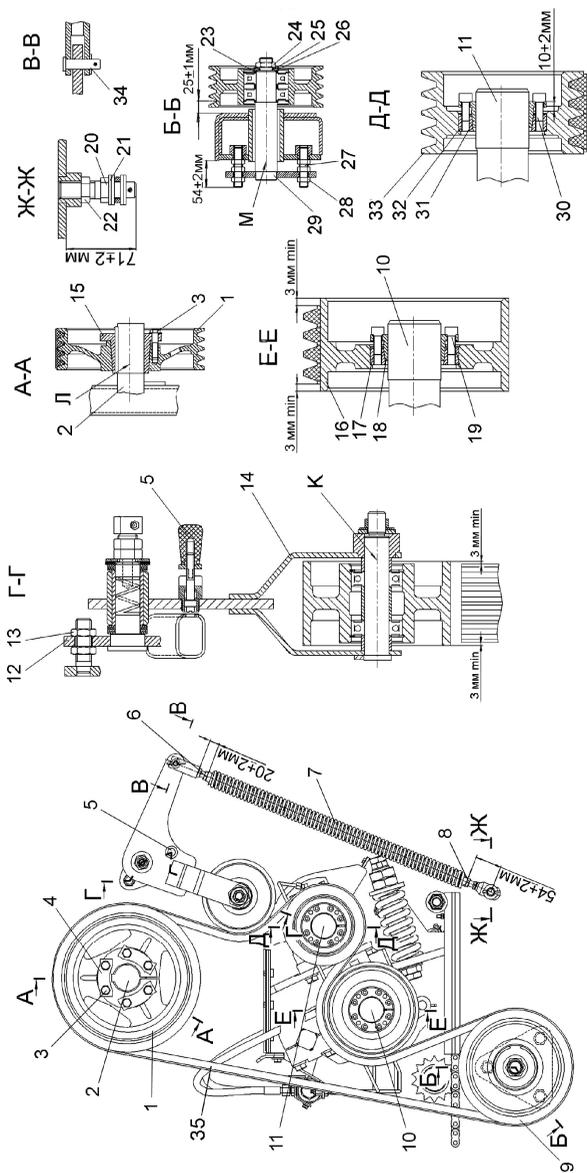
Схема регулировки привода дозимельчающего устройства:
